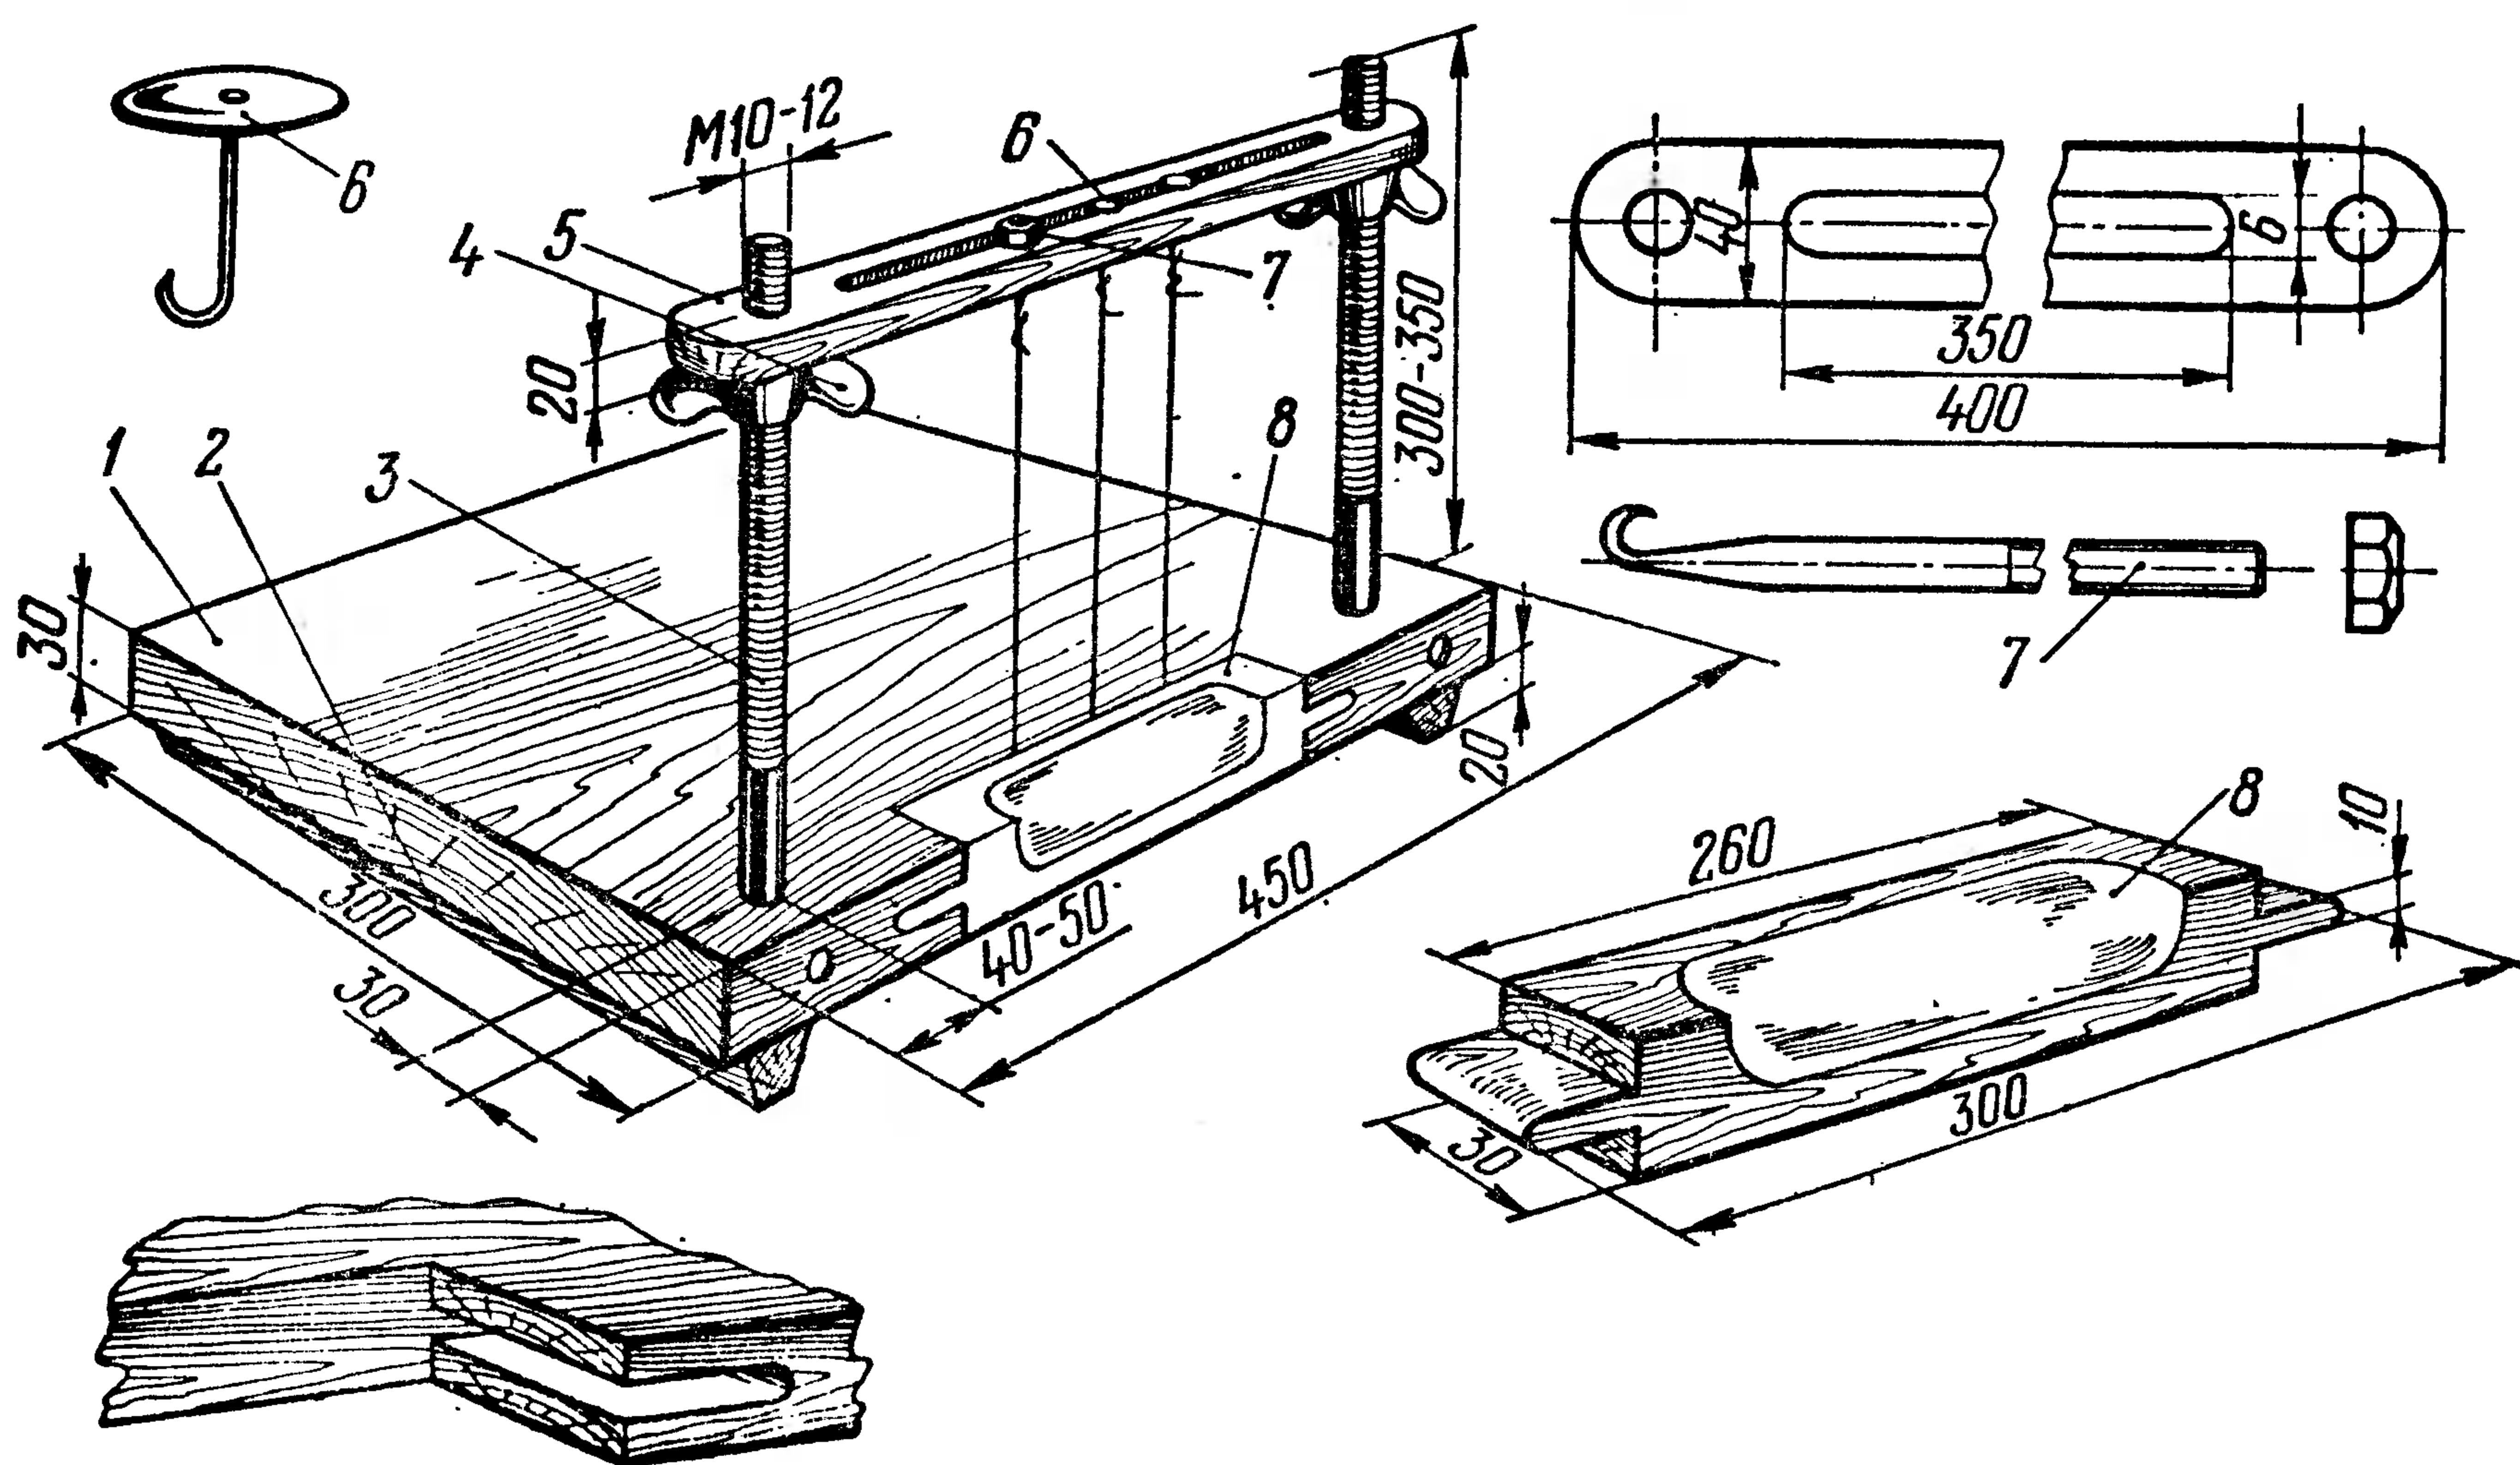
Сшивальный станок: 1 — основание; 2 — планка (ножка); 3 — вертикальная стойка с резьбой; 4 — гайка; 5 — перекладина; 6 — крючок для крепления шнуров; 7 — шпилька с крючком для натягивания марли, шнуров, тесьмы; 8 — съемная планка.
